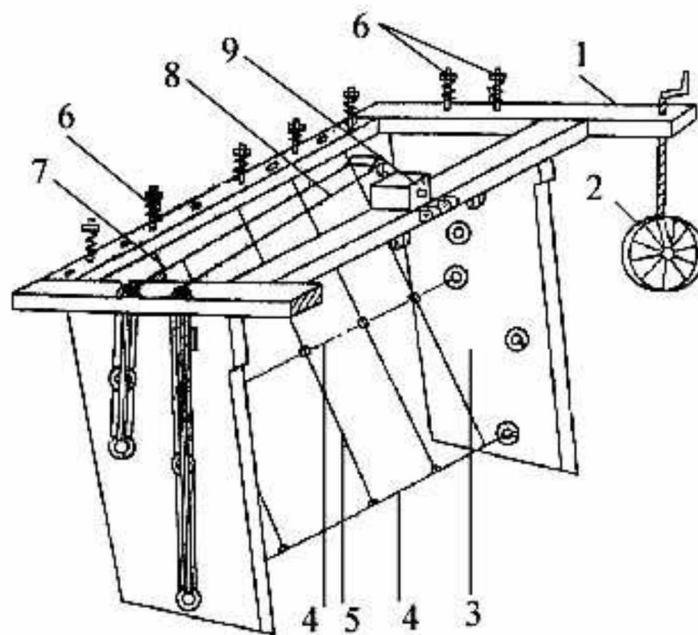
Розпушувач ґрунту: 1 – рама; 2 – опорна колесо; 3 – ніж-щілеріз; 4, 5 – робочий орган; 6 – регулювальний болт; 7, 8 – тяга; 9 – вібропривід
